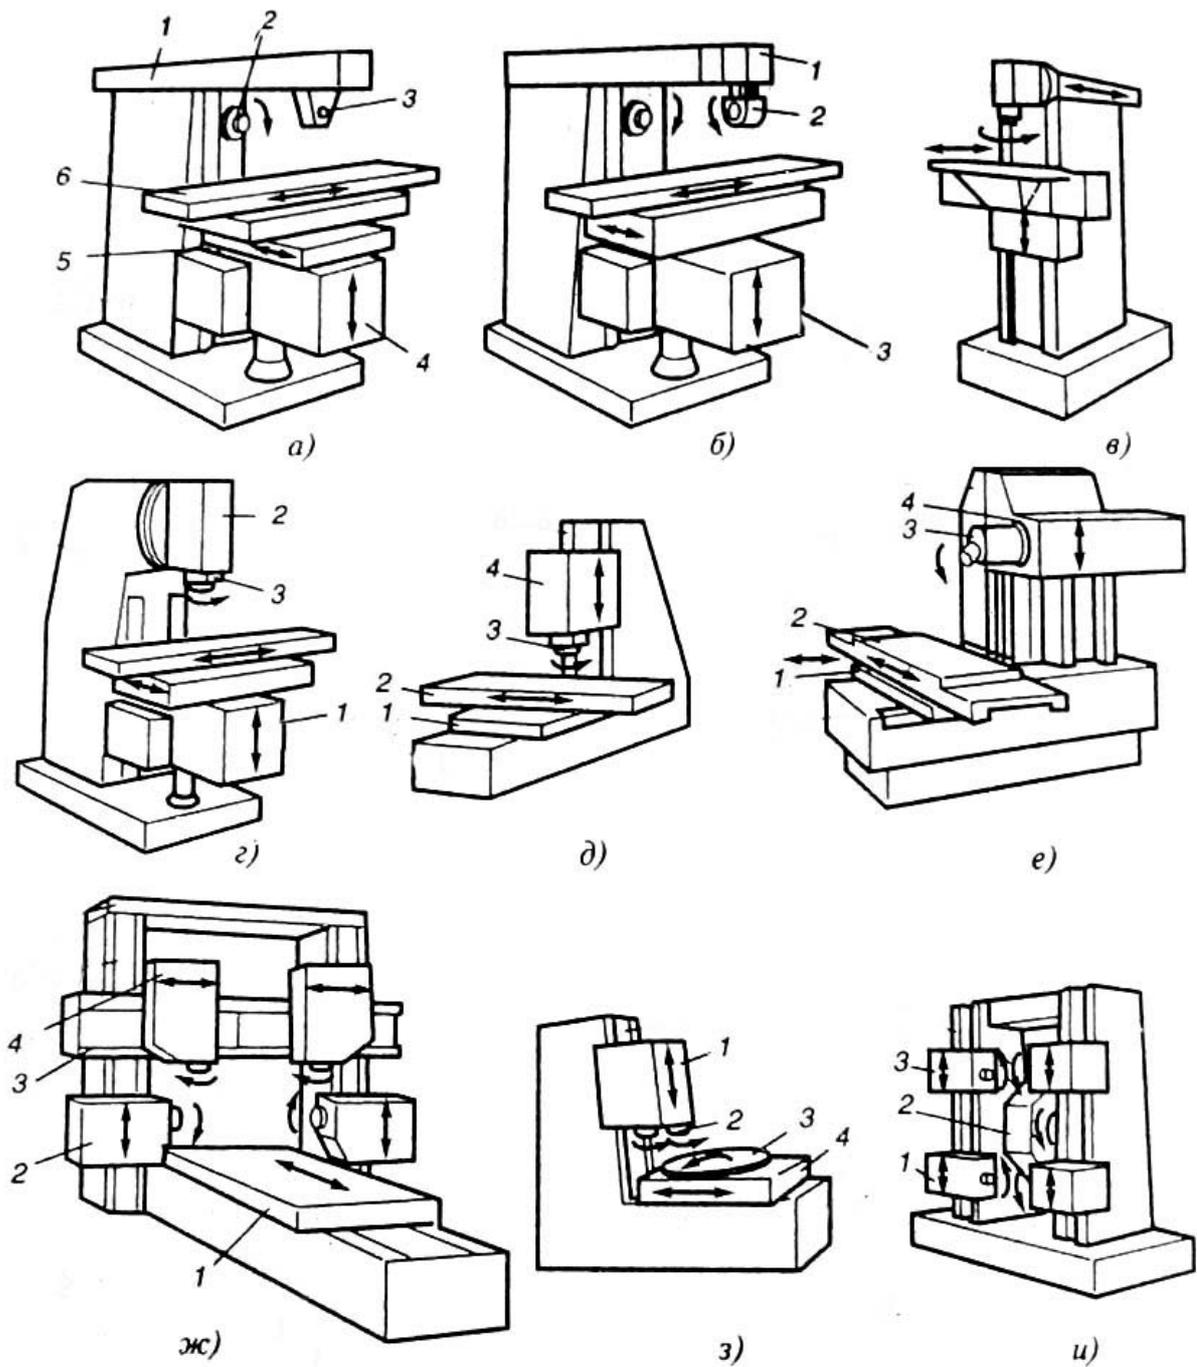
Станки фрезерные: *а* – консольный горизонтально-фрезерный: 1 – хобот выдвижной, 2 – шпиндель горизонтальный, 3 – серьга-опора, 4 – консоль, 5 – салазки, 6 – стол; *б* – широкоуниверсальный горизонтально-фрезерный: 1 – головка шпиндельная, 2 – головка накладная, 3 – консоль; *в* – широкоуниверсальный бесконсольно-фрезерный; *г* – консольный вертикально-фрезерный: 1 – консоль, 2 – головка шпиндельная, 3 – шпиндель; *д* – бесконсольный вертикально-фрезерный: 1 – салазки, 2 – стол, 3 – шпиндель, 4 – головка шпиндельная; *е* – бесконсольный горизонтально-фрезерный; *ж* – продольно – фрезерный; *з* – карусельно- фрезерный; *и* – барабанно-фрезерный
